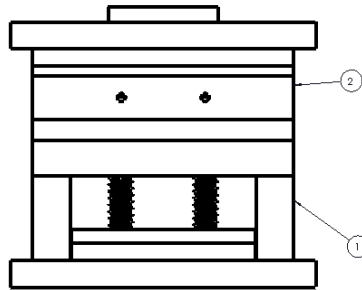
24 Molde de inyección 1) Parte móvil, 2) Parte fija
